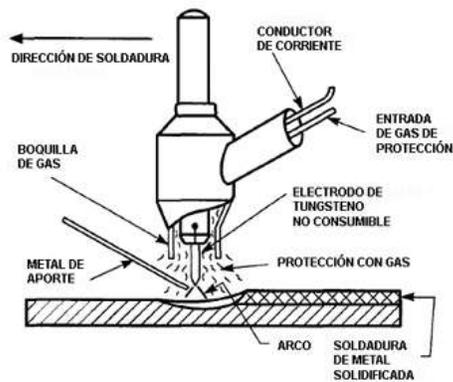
Figura que muestra la soldadura TIG aplicada al acero inoxidable.
